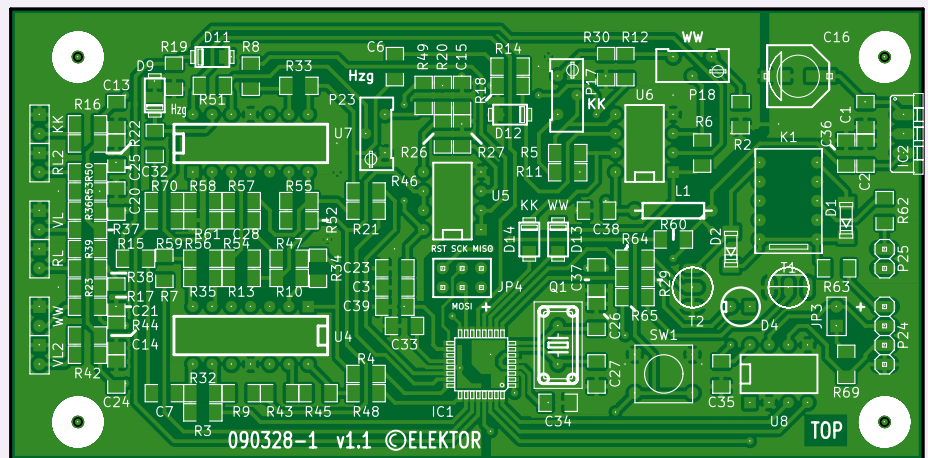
Bestückungsplan. Mit etwas Übung sind alle Bauteile noch von Hand zu löten.
